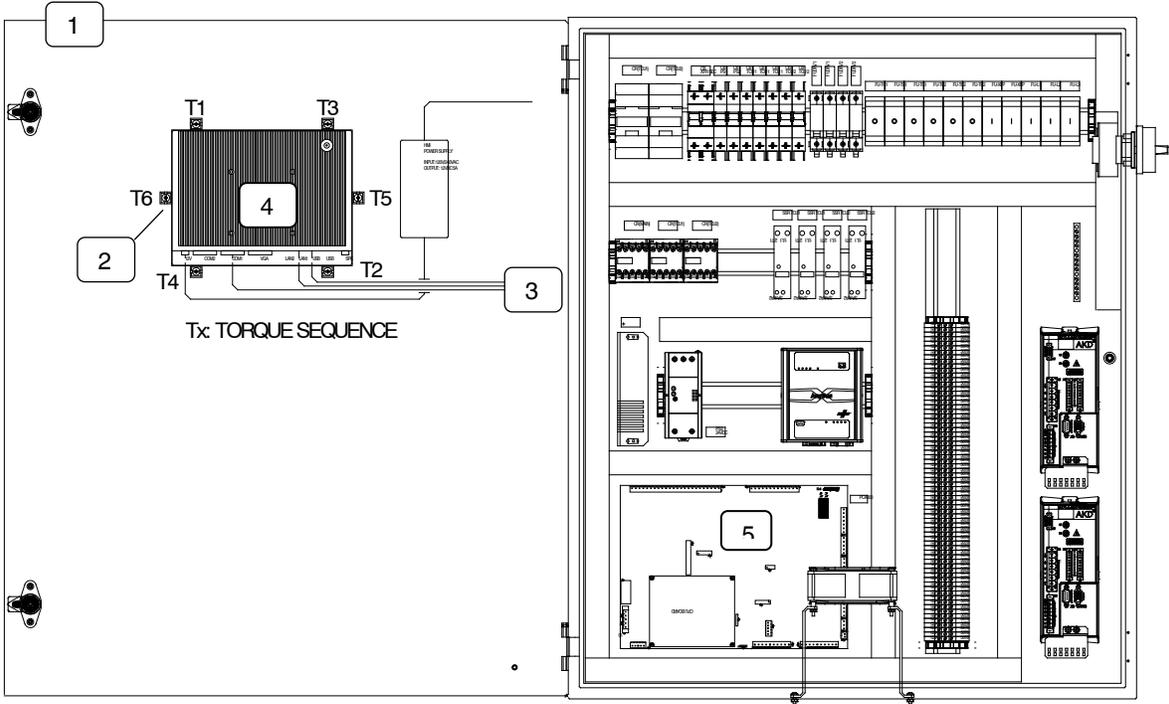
Benutzerschnittstelle und PCA ersetzen
